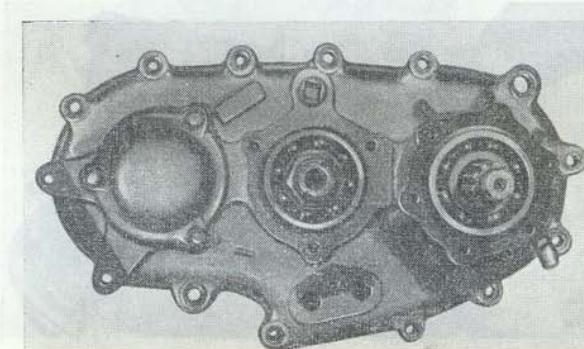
Валы раздаточной коробки, установленные в крышку картера
